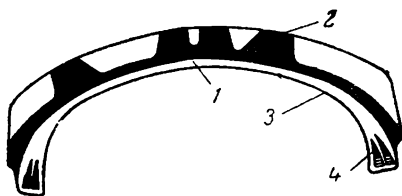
Профиль арочной шины: 1—каркас; 2—протектор; 3—герметизирующий слой; 4—бортовые кольца.
